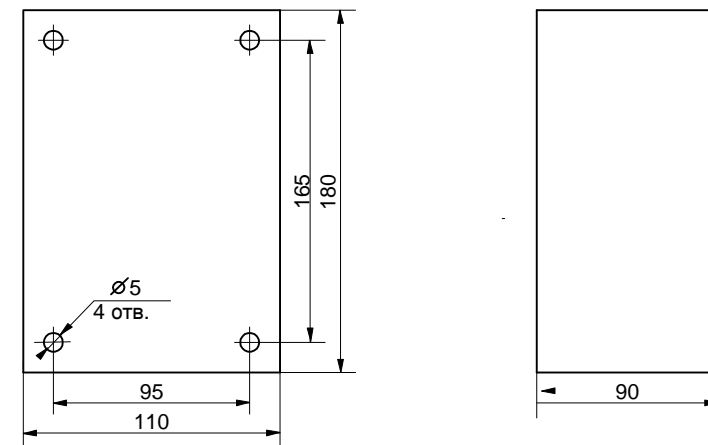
Габаритные и установочные размеры устройства УЗОПК-3.
